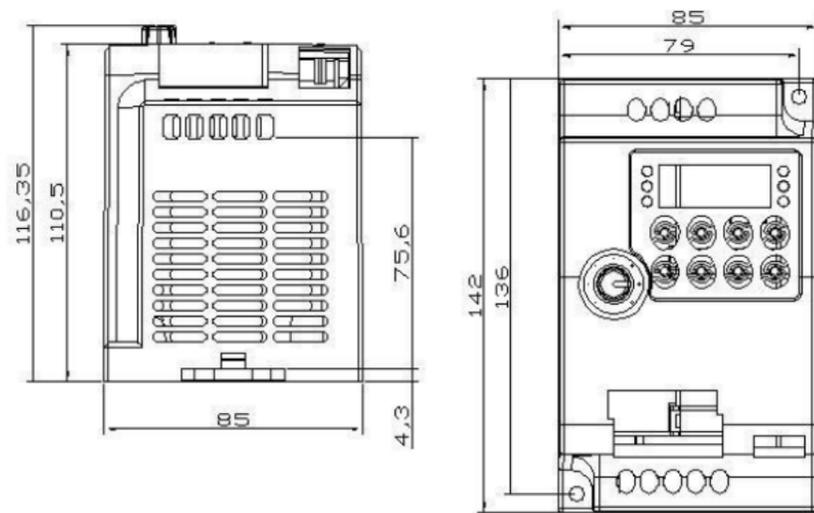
AC360 塑胶结构外型尺寸及安装尺寸示意图
